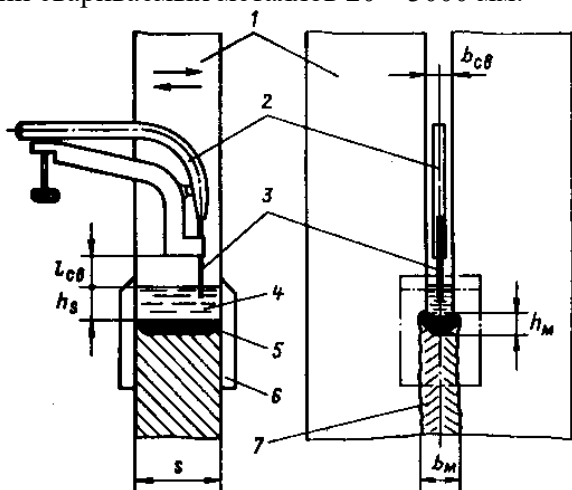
Схема электрошлаковой сварки:
